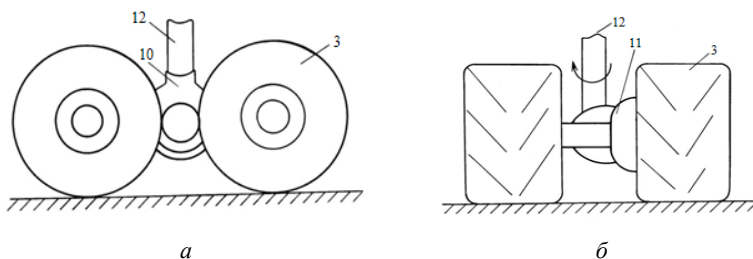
Каретка з колесами: *a* – загальний вид збоку; *б* – вид спереду; 3 – колеса; 10 – каретка; 11 – гідравлічний привод; 12 – центральна вісь
